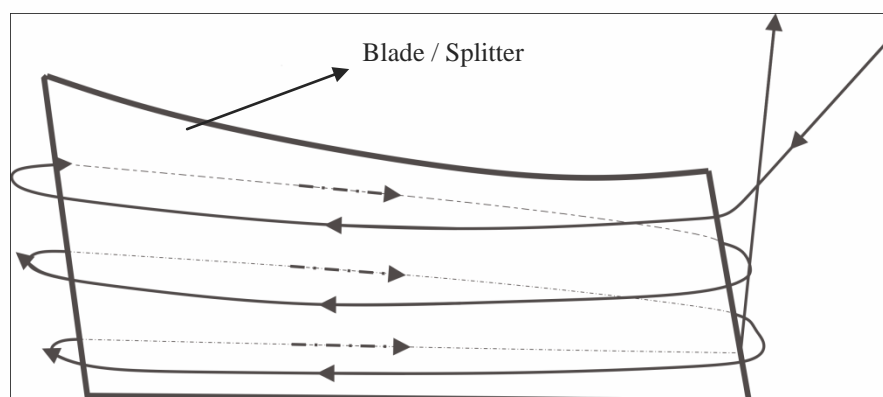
kemungkinan *interference* antara *cutting tool* dengan *workpiece* pada proses finishing *blade impeller* diameter 27 mm
